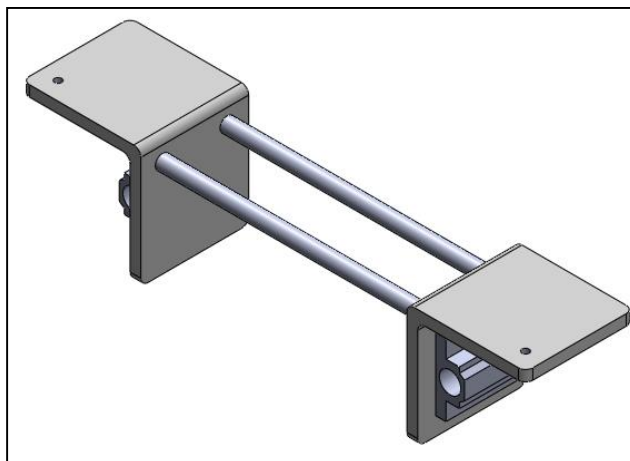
Vista isométrica del ensamblaje 1 de la máquina cortadora de vidrio
